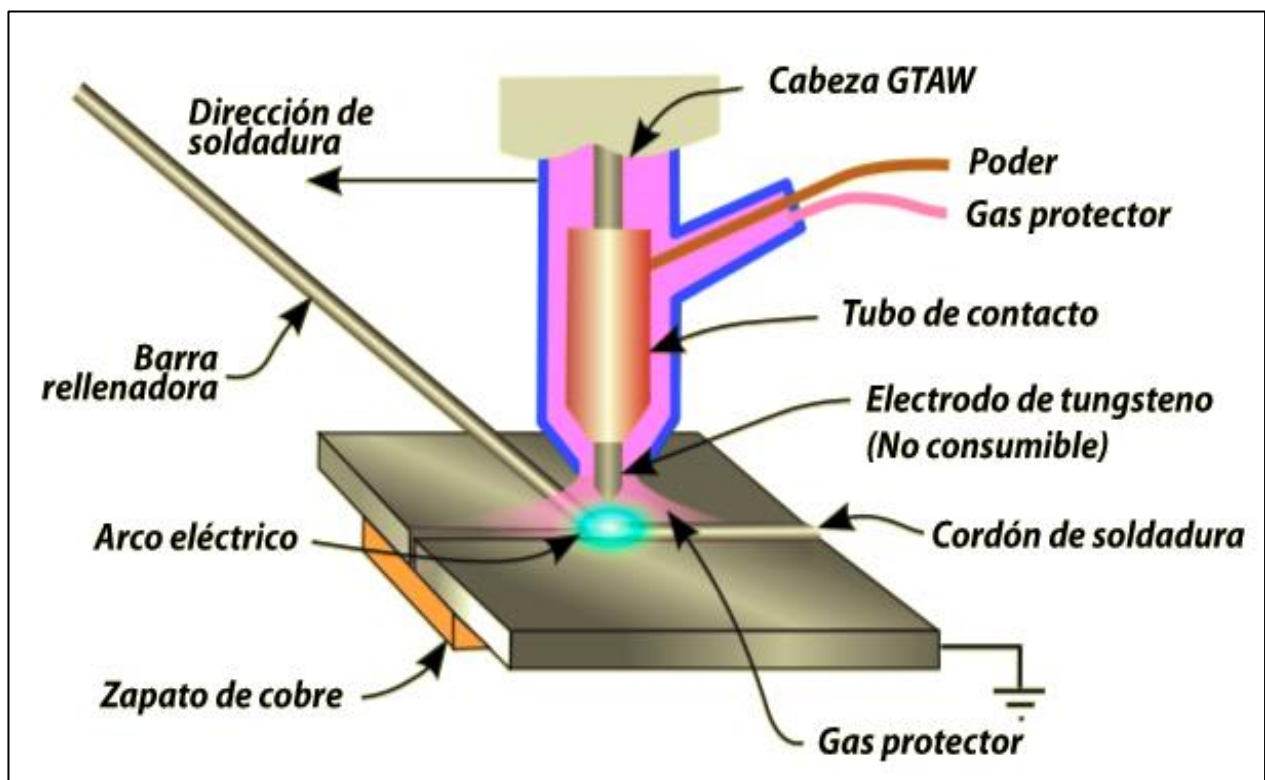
Esquema del proceso de soldeo TIG/GTAW. Fuente: Equipos y soldaduras RAFE.
